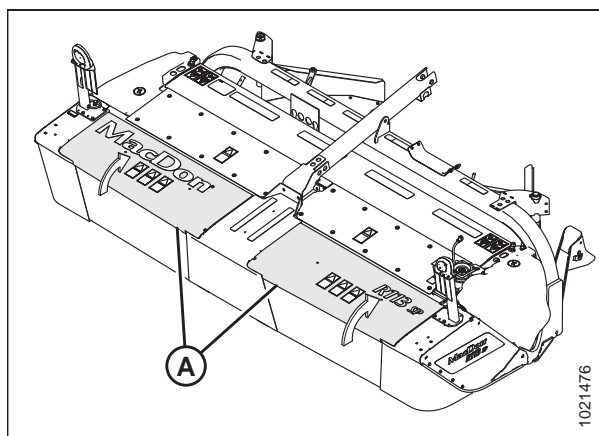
Щитки ножевого бруса – R113 SP
